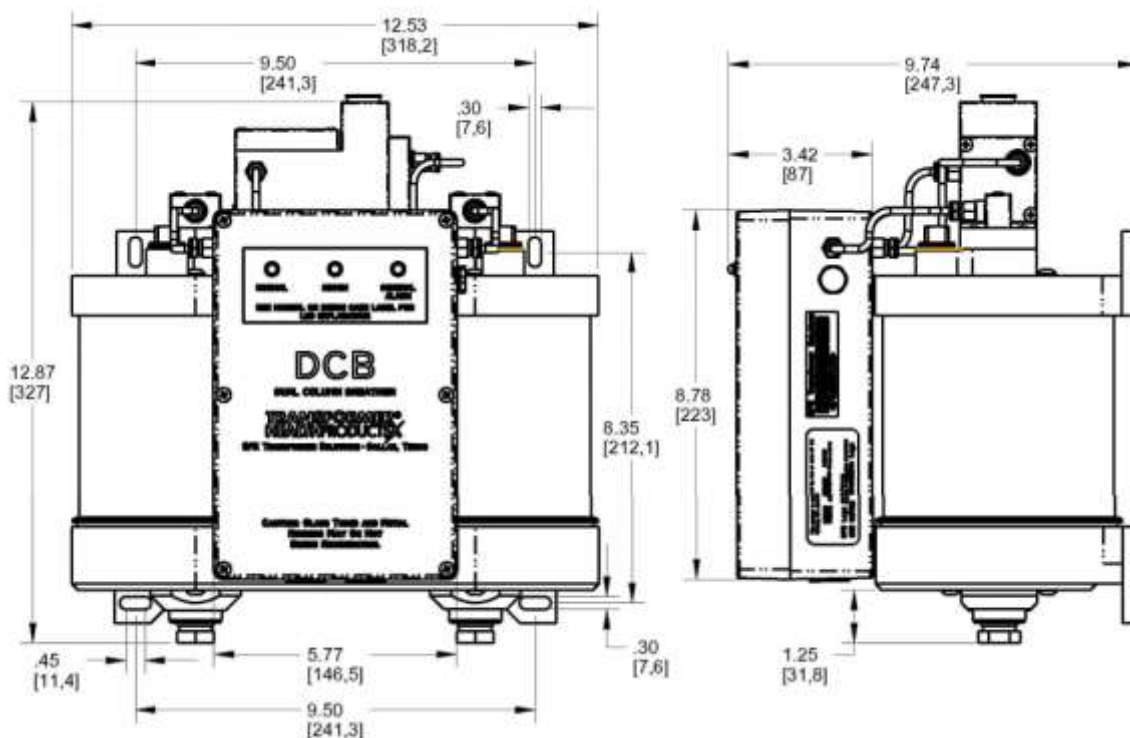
Dimensiones de Montaje de DCB, pulgadas [mm]
